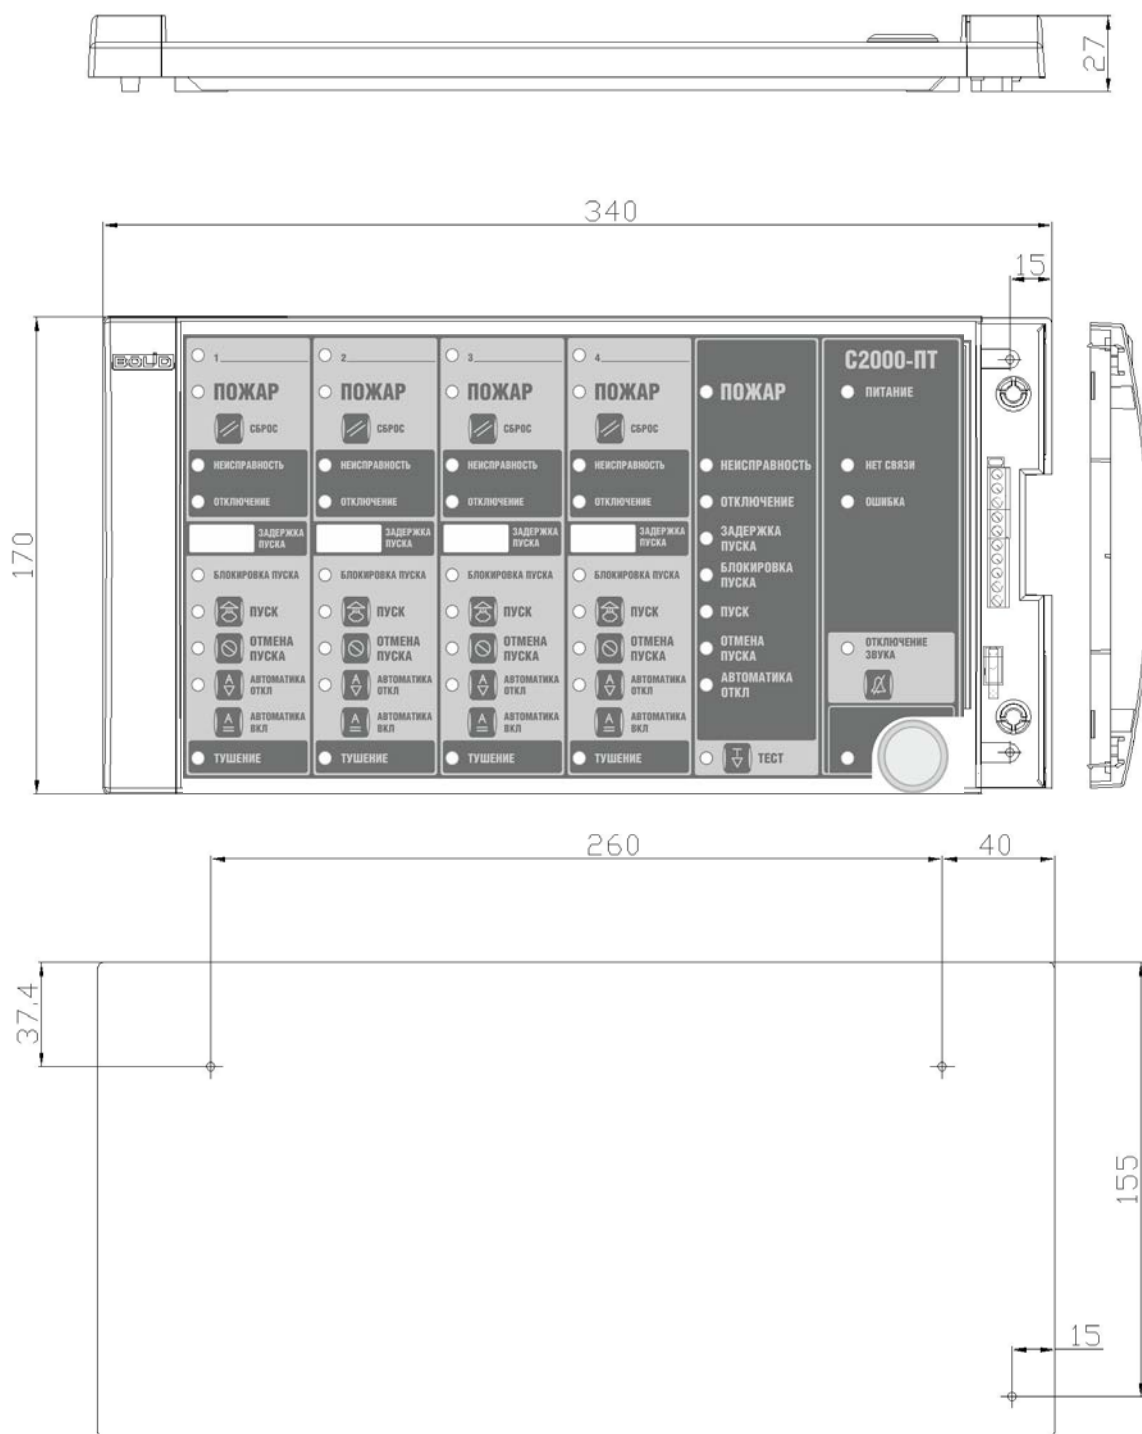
Внешний вид, габаритные и установочные размеры блока «С2000-ПТ»
